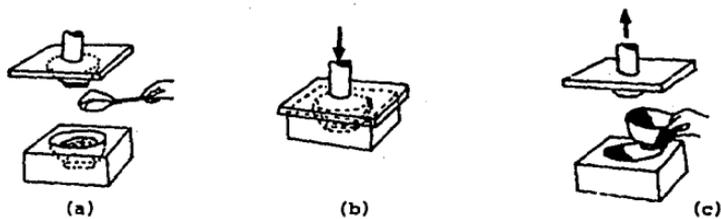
MOLDEADO A COMPRESION.
